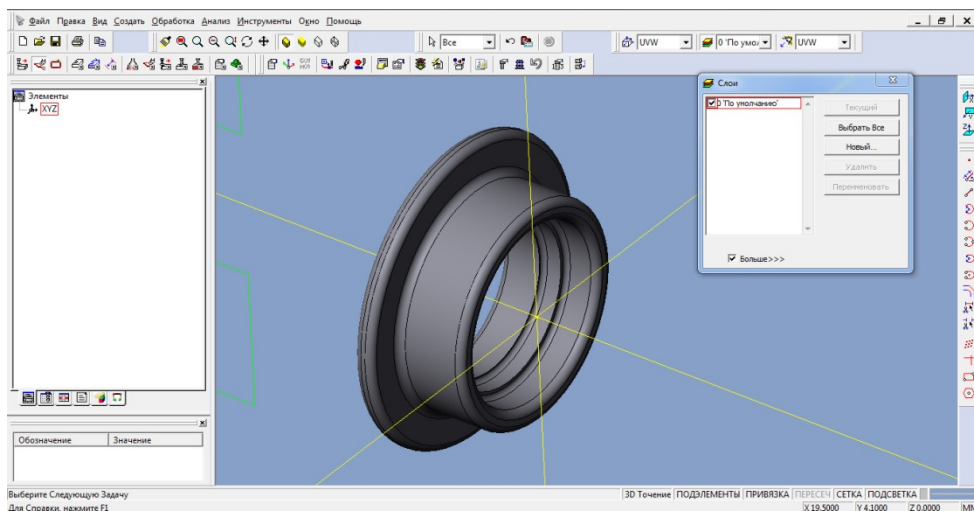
3D модель заготовки корпусу у середовищі Esprit
